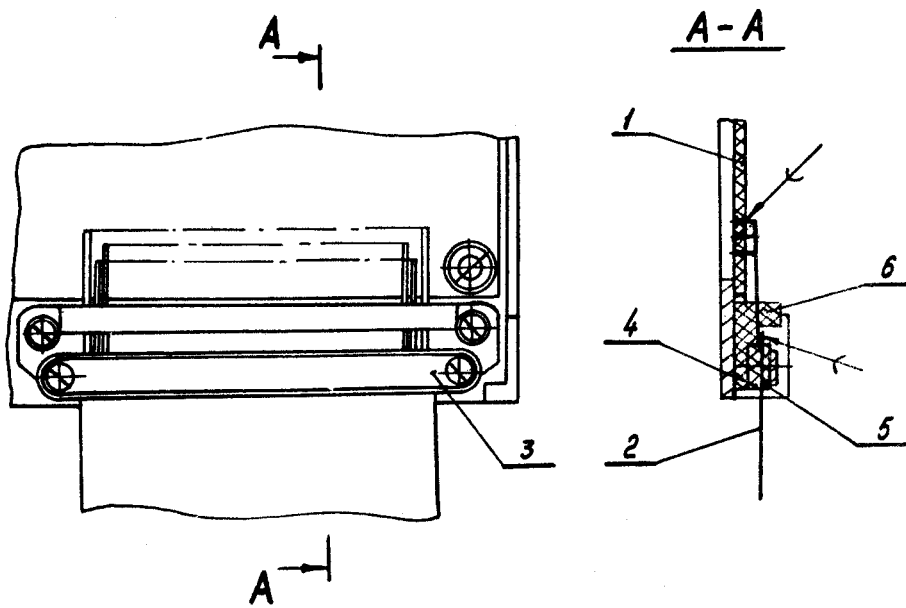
Гибкий печатный кабель с колодкой и его установка на печатную плату: 1 - плата печатная; 2 - кабель гибкий печатный; 3 - планка прижимная; 4 и 5 - прокладки; 6 - колодка
